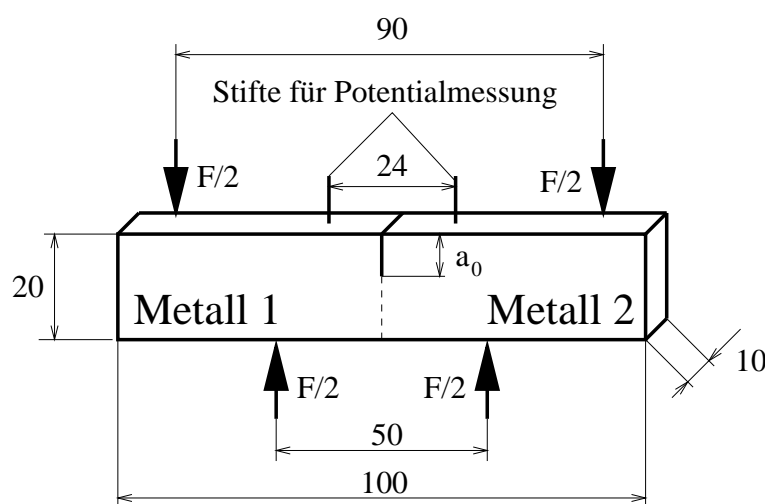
Geometrie einer Vierpunktbiegeprobe aus einem explosionsgeschweißten Materialverbund
